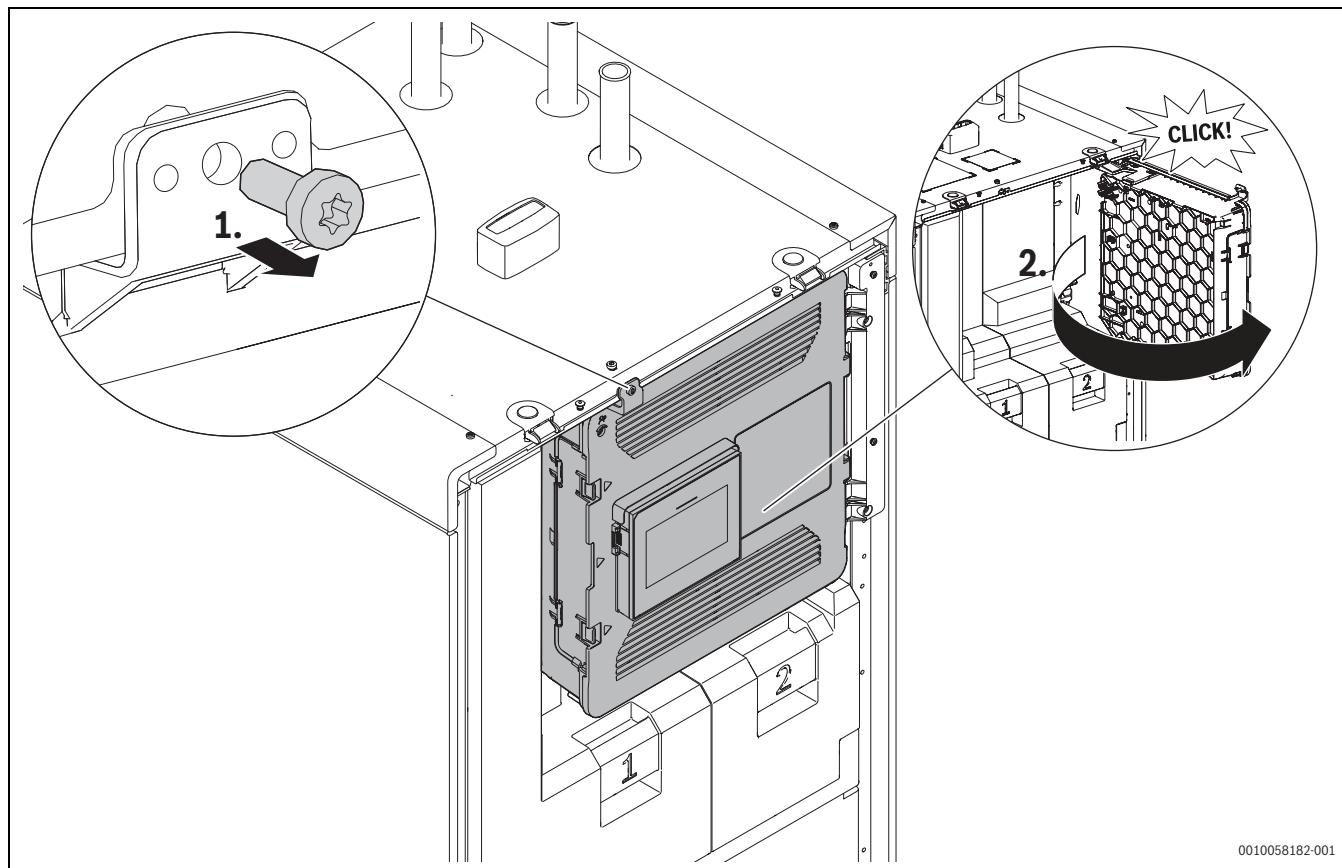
Vorderansicht: Klemmenkasten mit Sicherungsschraube
